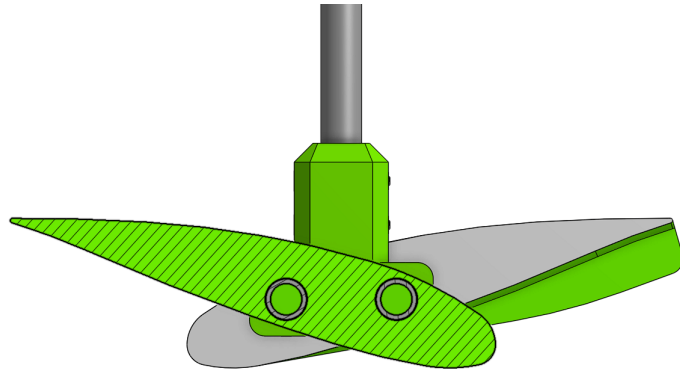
Vista lateral del ensamblaje de la hélice con vista de sección en Onshape [fuente: elaboración propia]
